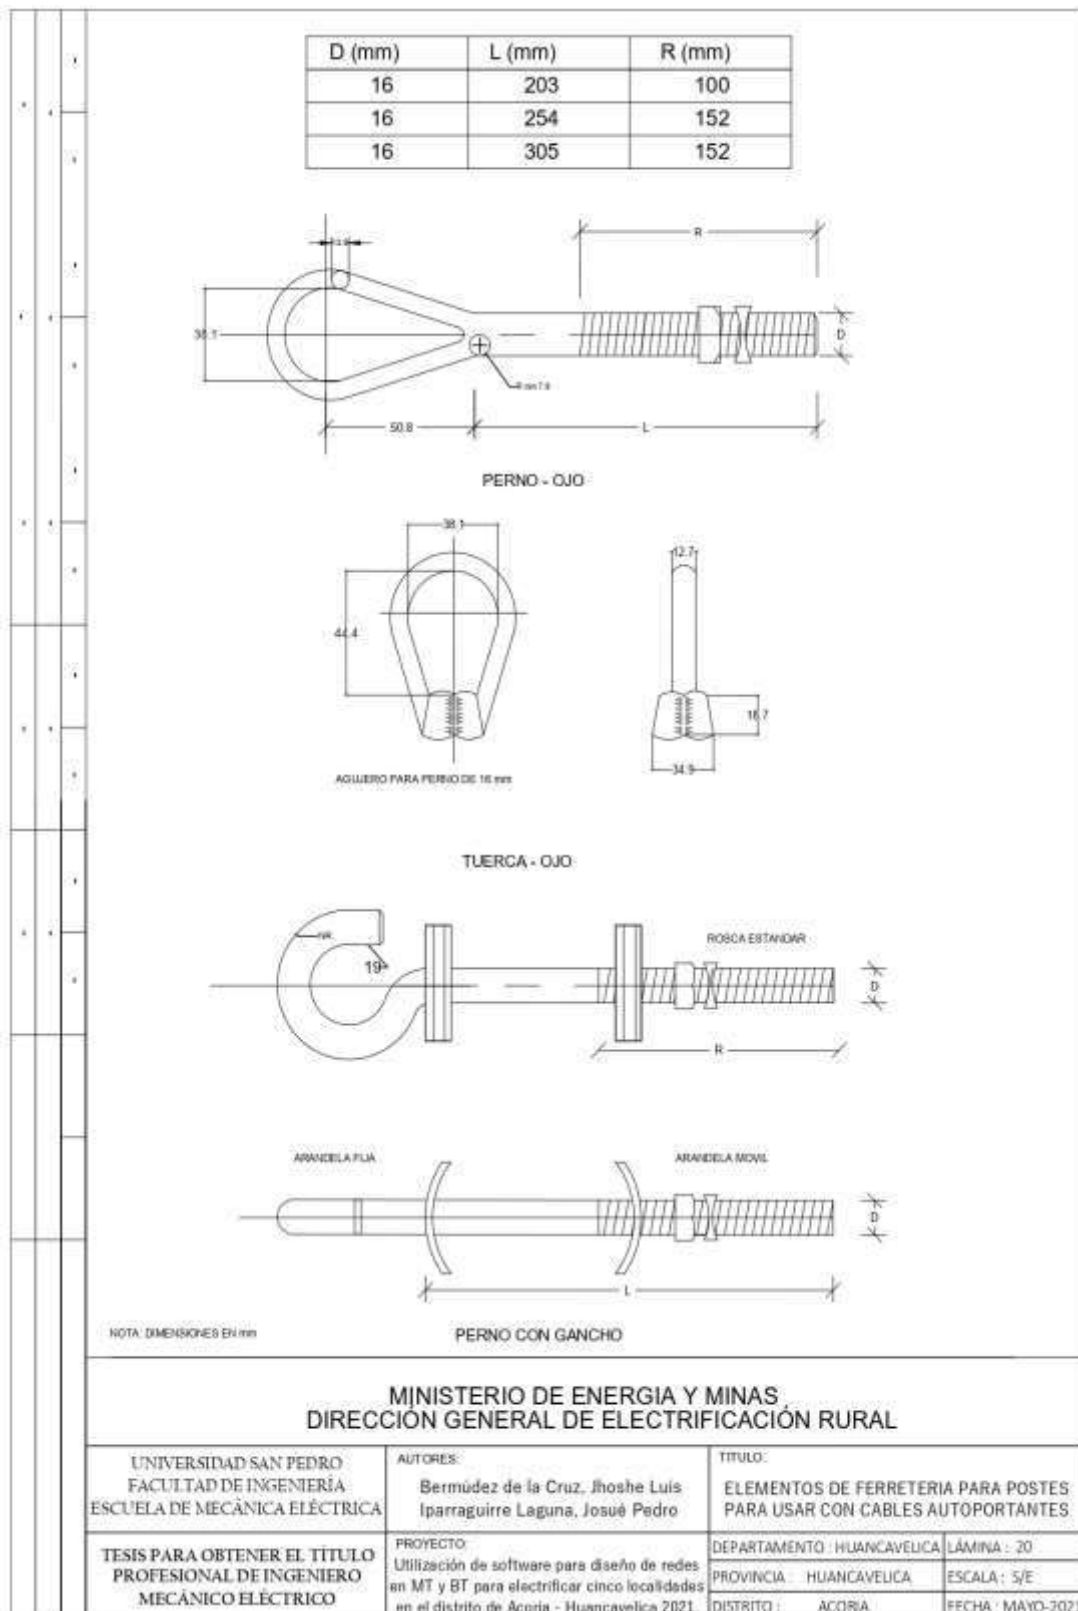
Lamina de detalle 20, elementos de ferretería para postes para usar con cables autoportantes
